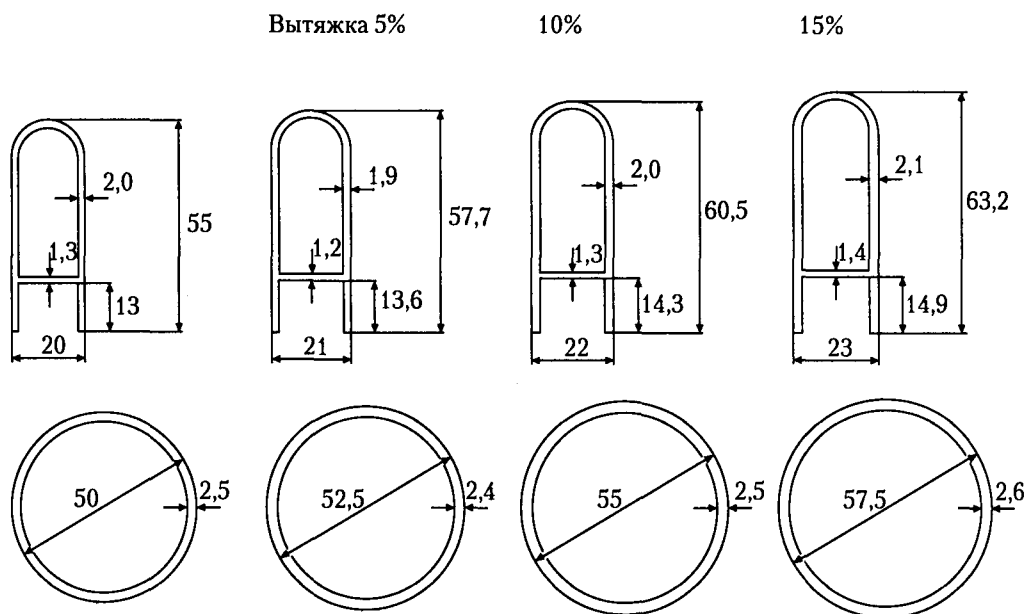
Размеры формирующего отверстия для экструзии труб и профилей из ПК
